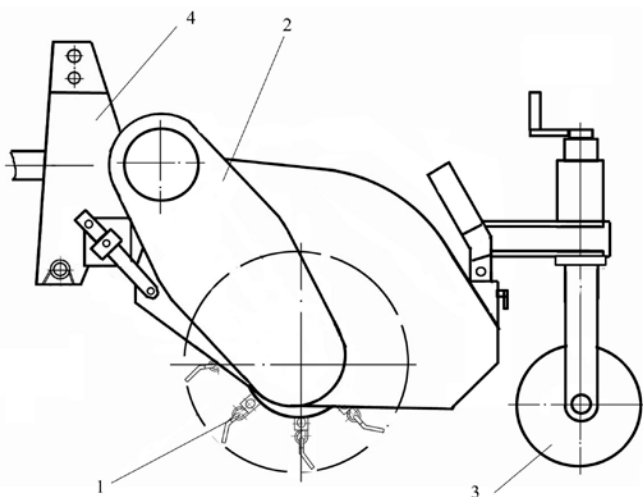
Конструктивная схема косилки-измельчителя для пастбищ КИ-3: 1 – ротор; 2 – редуктор; 3 – каток; 4 – рама
